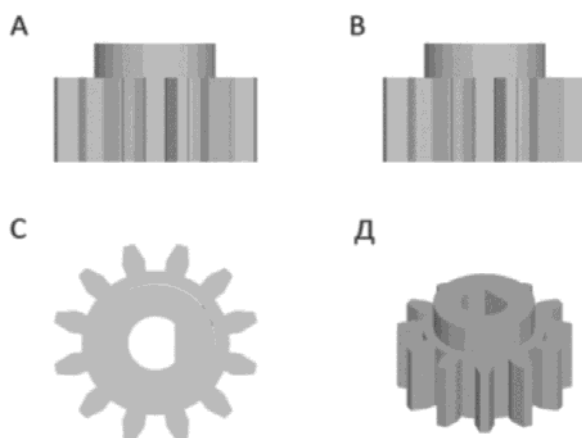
Шестерня вала двигателя: А – вид спереди; В – вид слева; С – вид сверху; Д – общий вид
